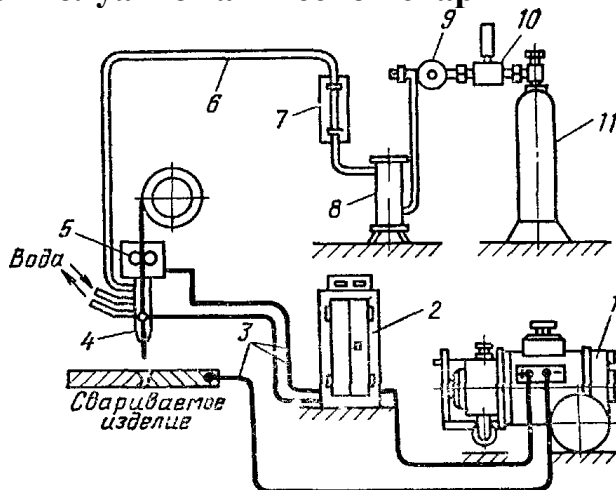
Схема поста для полуавтоматической сварки плавящимся электродом в среде защитного газа
